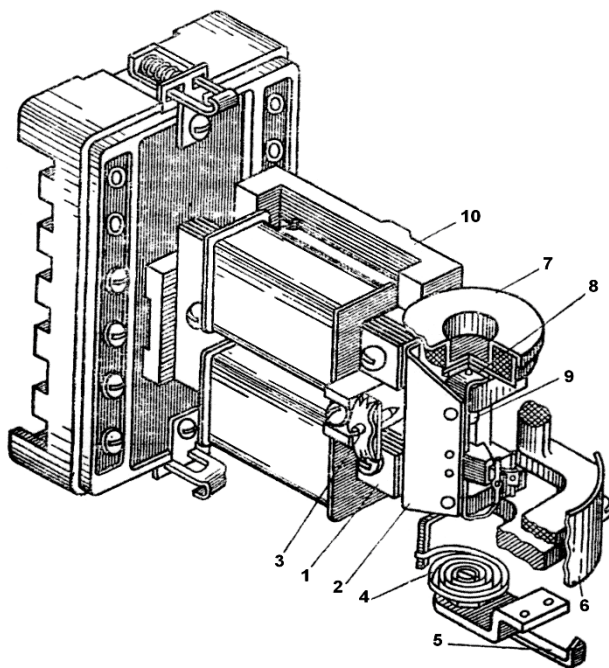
Кінематична схема реле з поворотним якорем типу РТ-40
